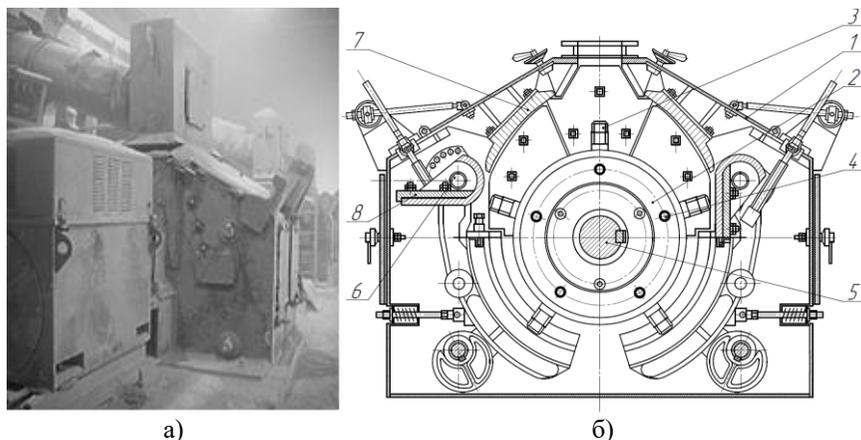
Общий вид (а) и схема (б) дробилки ДМРиЭ 14,5×13
